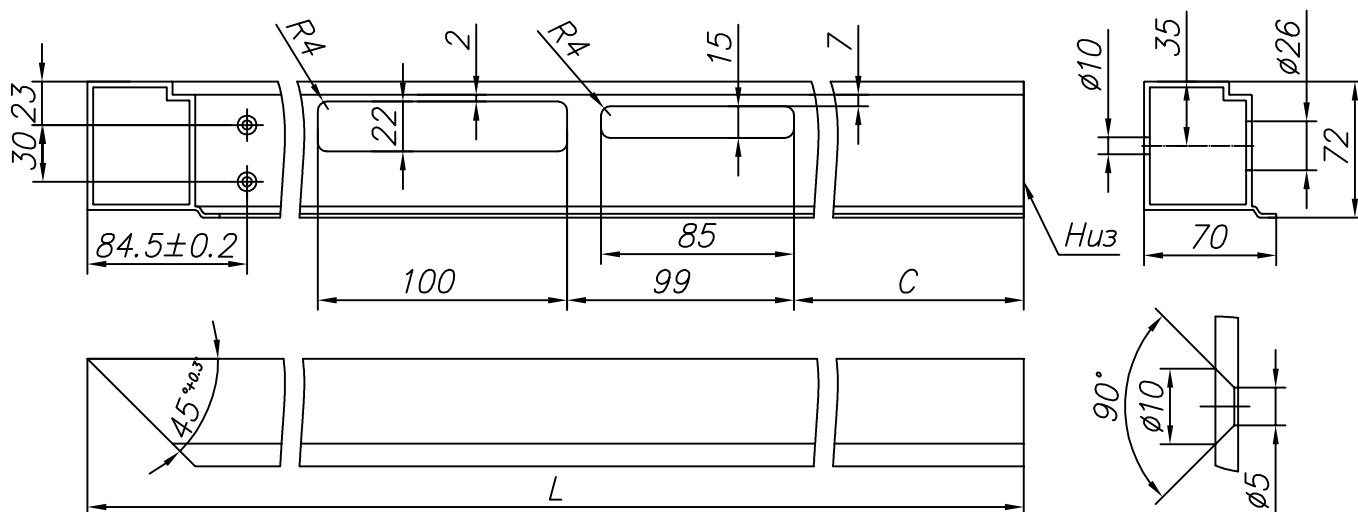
Изготовление столба притвора с пазом для автоматической защелки 118WE для калитки с перекладиной (открывание влево)
